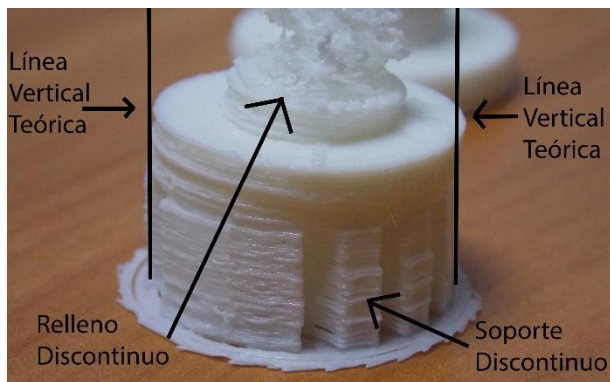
Pieza impresa bajo los parámetros recomendados por fabricante.
